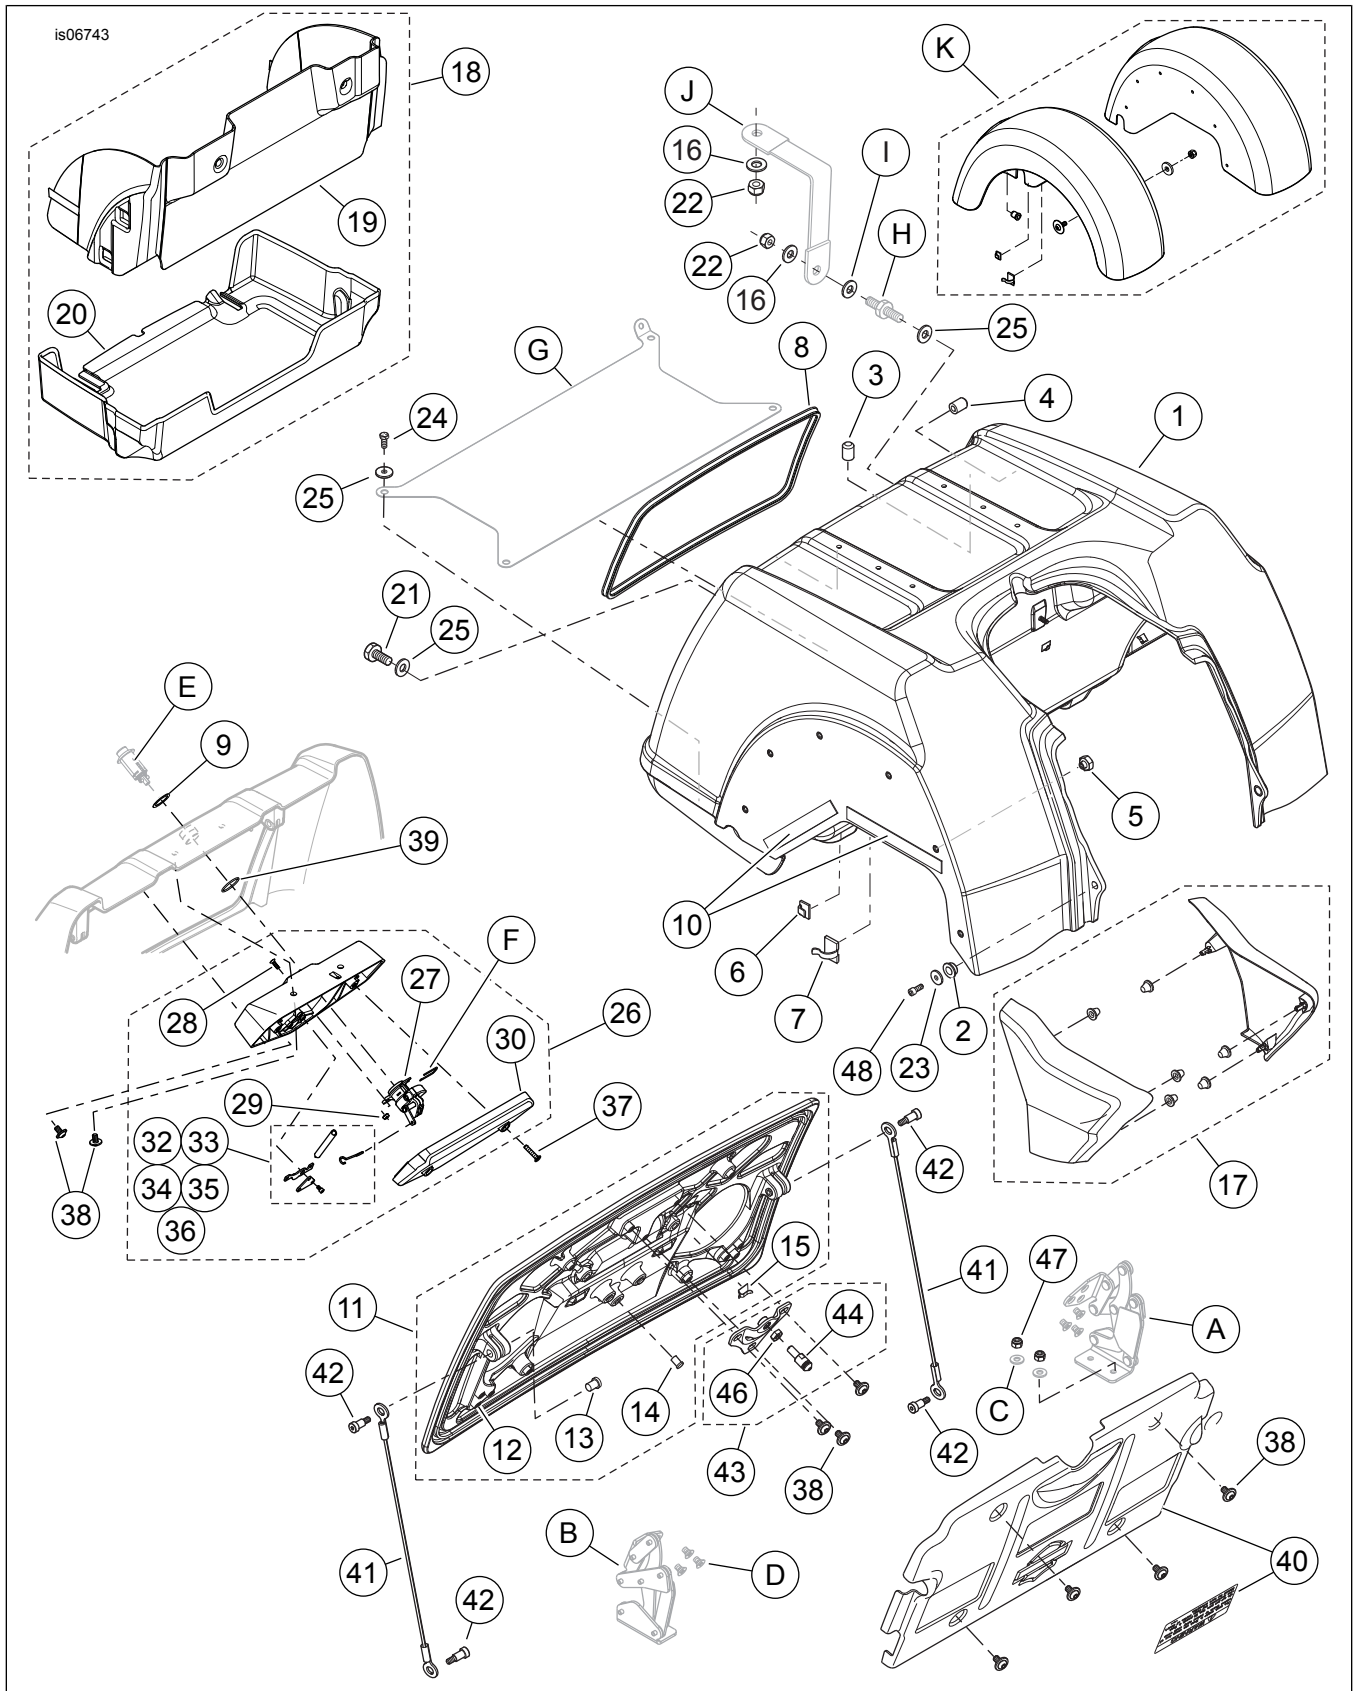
Pièces détachées, kits de corps de remplacement Trike
